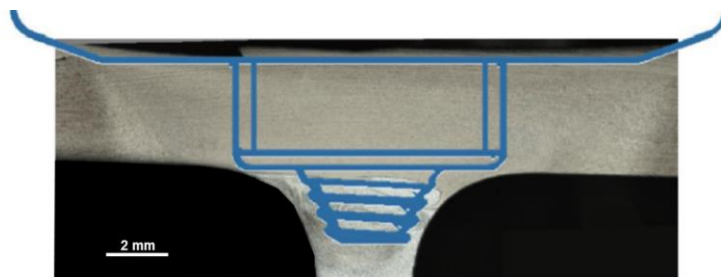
Posição relativa da ferramenta e da matriz durante a soldadura.
